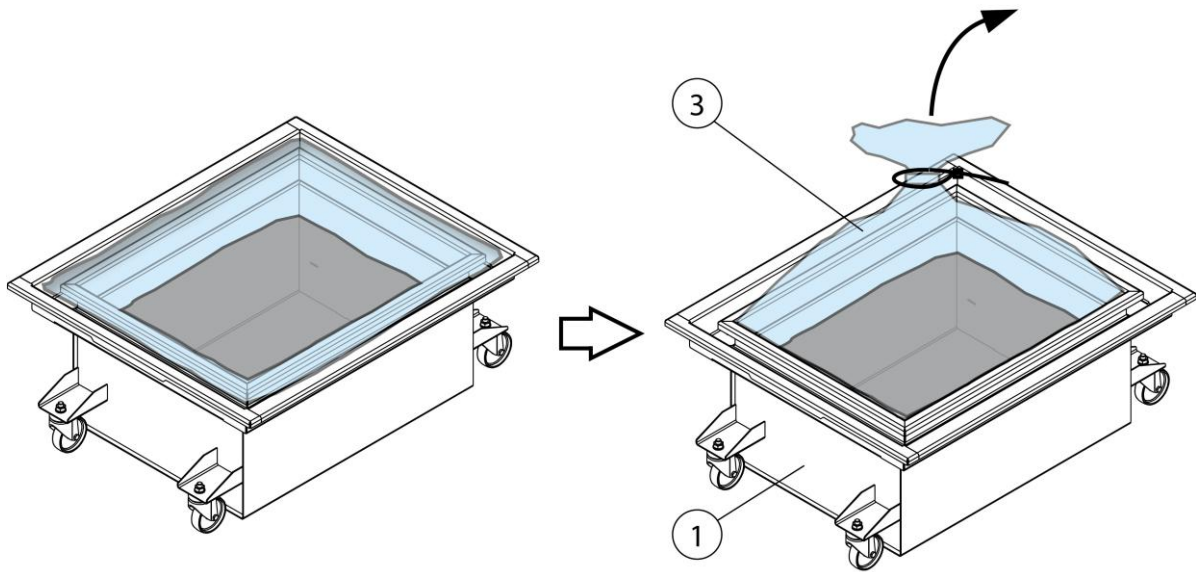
Wartung - Entleeren des Staubsammelbehälters
